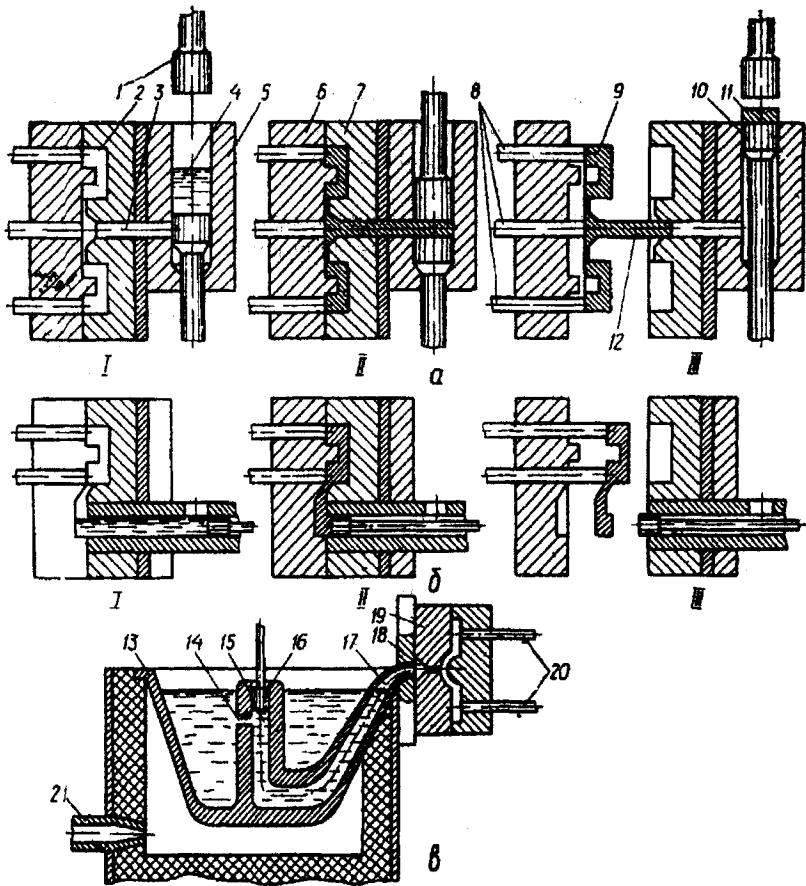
Схеми поршньових машин для лиття під тиском
